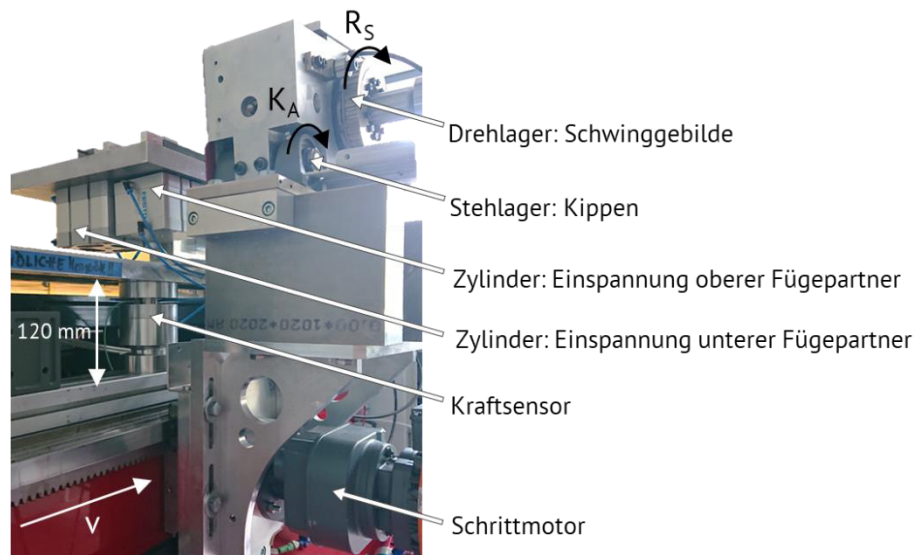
Aufbau der Translationsschweißanlage auf der Rückseite
